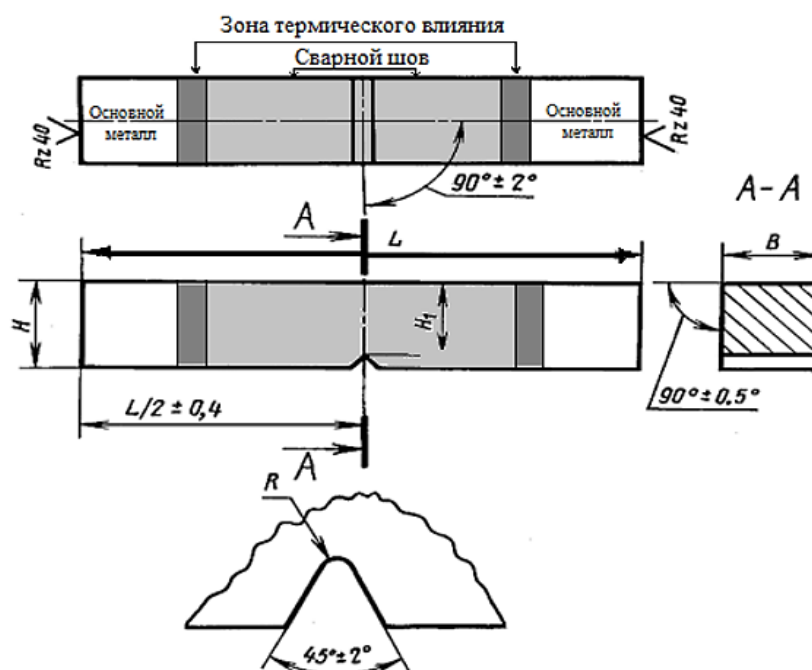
Образец МШ для испытаний на ударный изгиб
